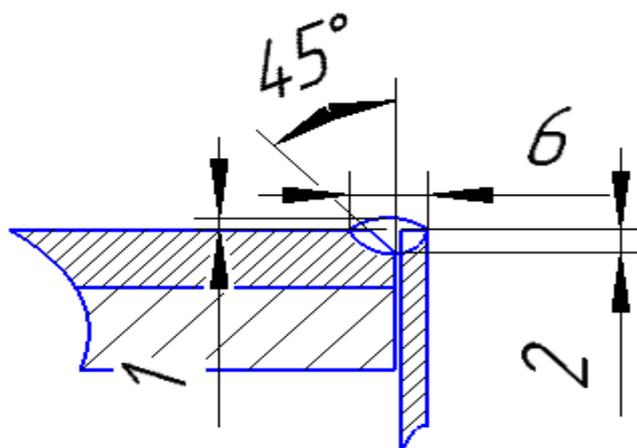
Эскиз нестандартного стыкового сварного соединения труб с трубной решеткой
